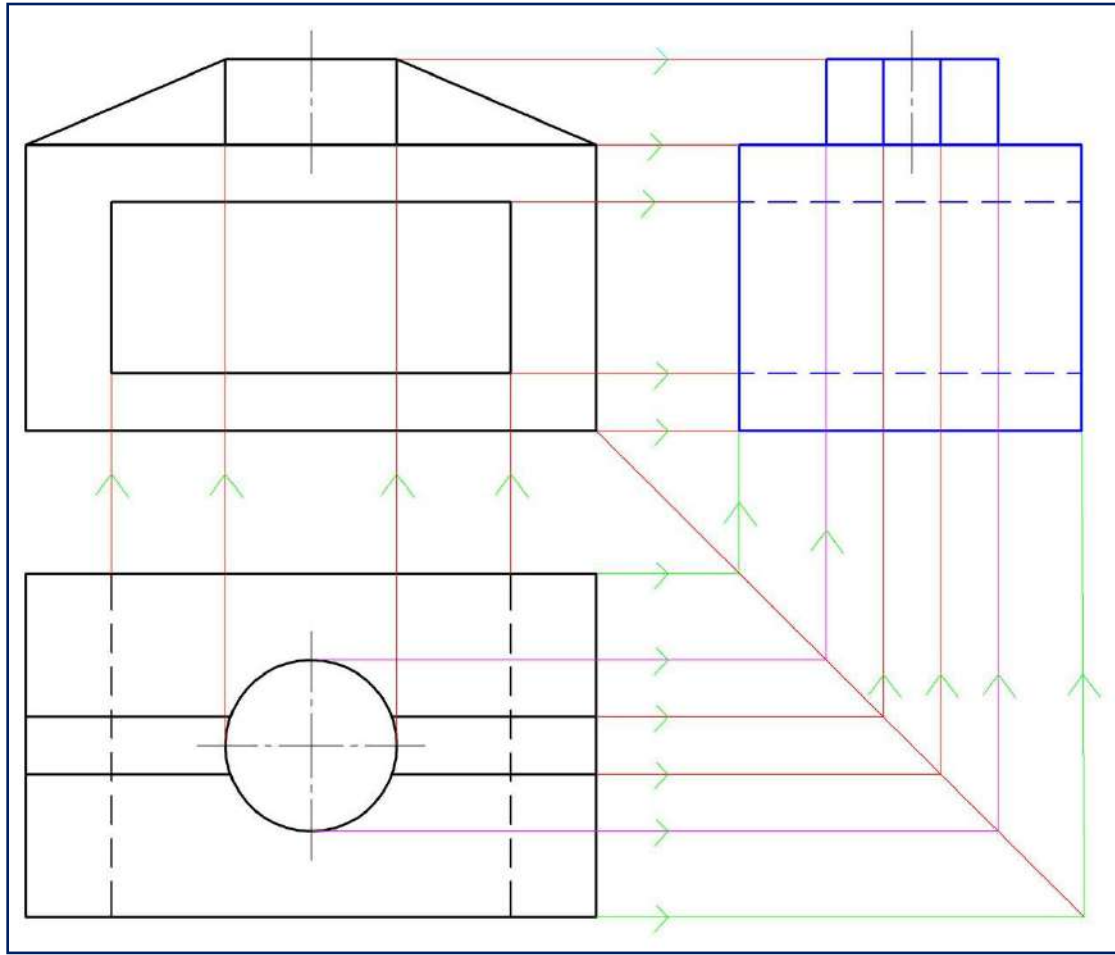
أ المسقط الأمامي والمسقط الأفقي لجسم
